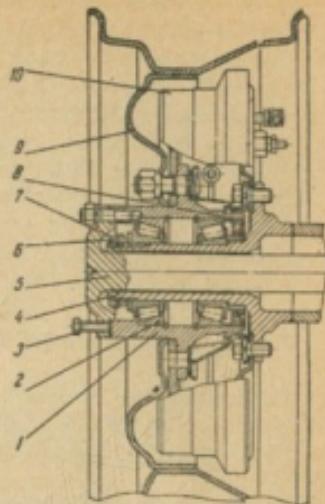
Ступица заднего колеса автомобиля УАЗ-469:
